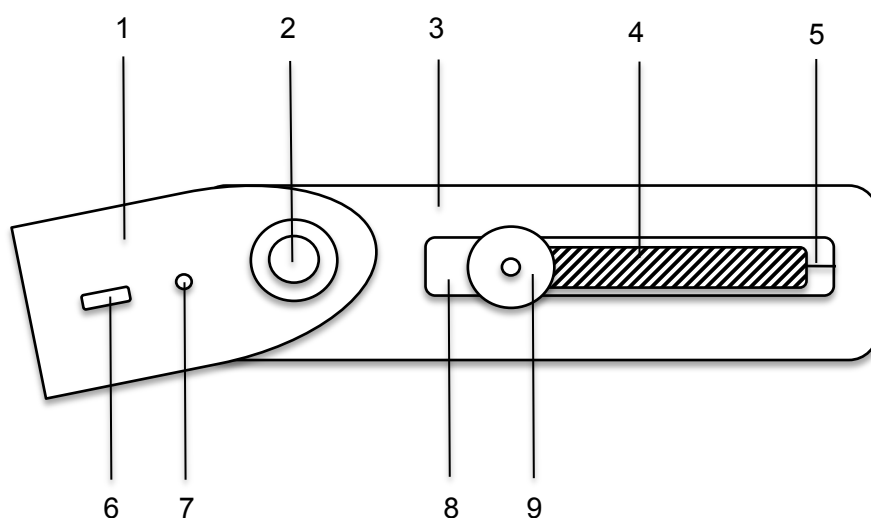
Technische Zeichnung des Prototypen mit Bezeichnung der Bauteile
